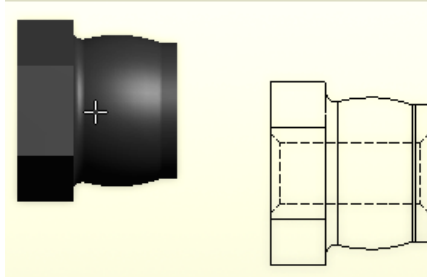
Tampilan Toolbar *Place Views* pada Inventor Drawing
